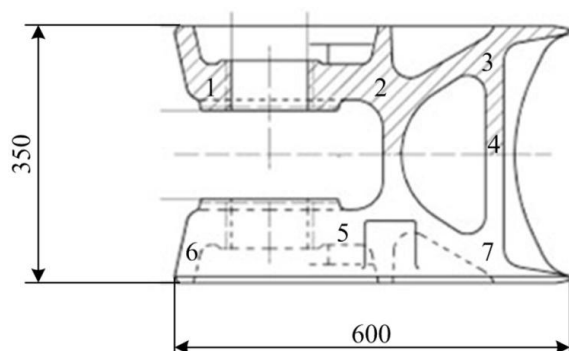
«Корпус подшипников» с габаритными размерами. Масса 360 кг; сталь 20ГЛ; (1–7) – контрольные точки исследования структуры и механических свойств
